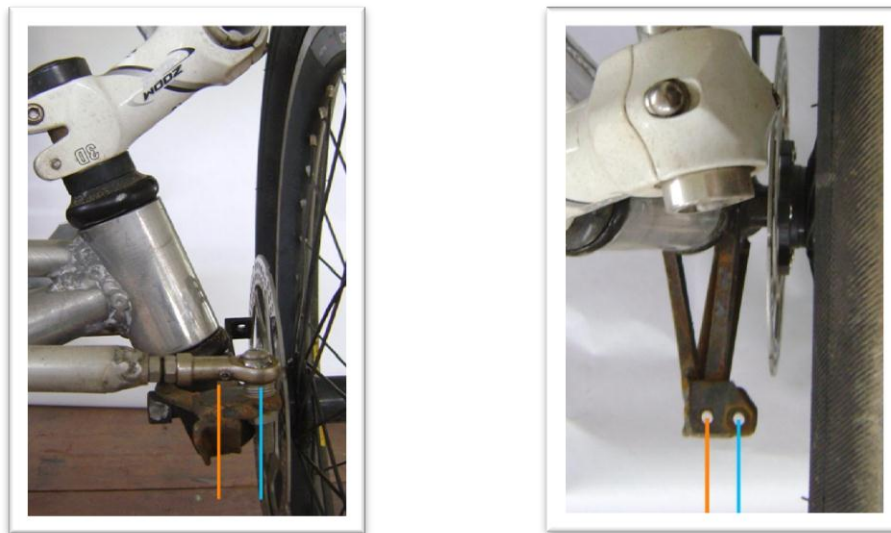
Vistas frontal y superior del brazo secundario. A la izquierda se observa las líneas naranjas que muestran la posición previa del punto de sujeción de la terminal y las líneas azules la posición definitiva. Fuente: Franklin Patiño.
